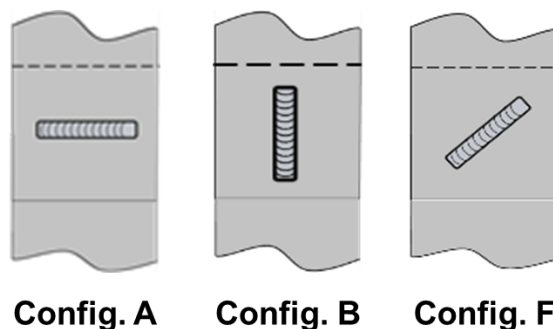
Configurations du cordon de soudure des joints soudés
